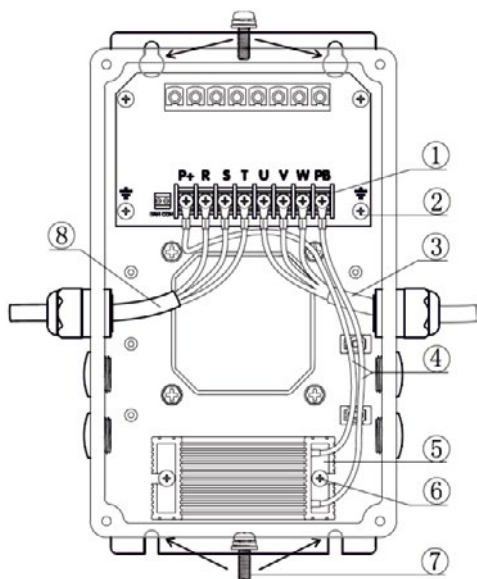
Установка соединительной коробки и подключение силовой цепи
